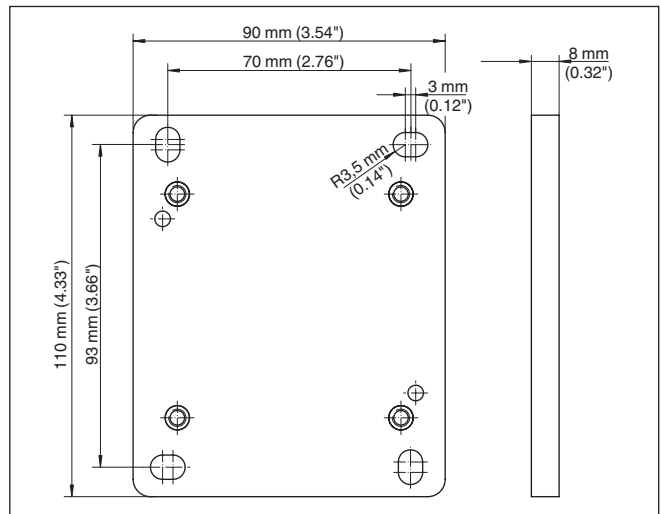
Plantilla para taladrar - Placa de montaje en la pared
